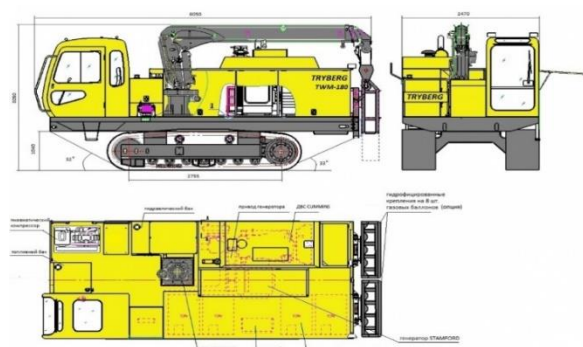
Габариты и компоновка самоходного сварочного агрегата TWM-180 TRYBERG [19]
